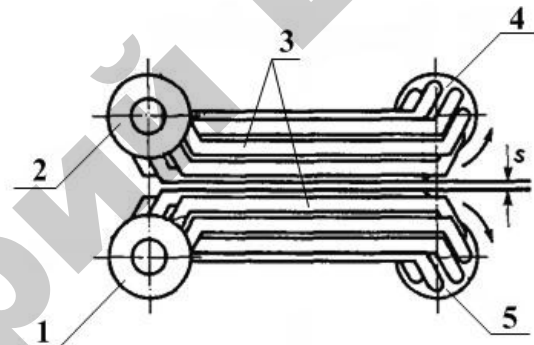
Роторно-планчатый очесывающий аппарат:
